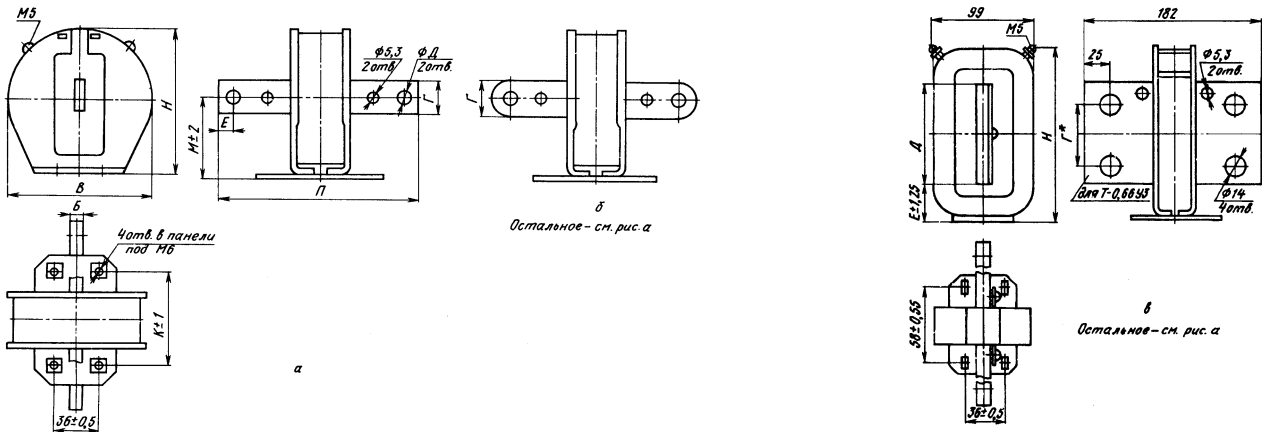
Габаритные, установочные и присоединительные размеры трансформаторов тока Т-0,66 и ТШ-0,66
